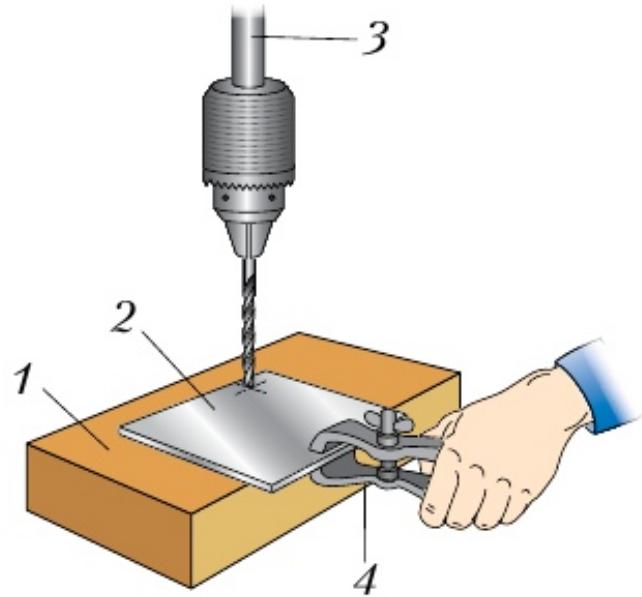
Сверление заготовки на подкладной доске: 1 – подкладная доска; 2 – заготовка; 3 – шпиндель станка; 4 – ручные тиски
